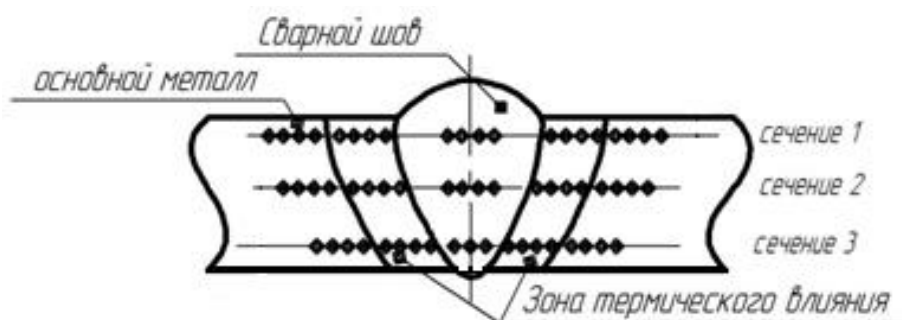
Схема измерения твердости по сечениям сварного соединения
